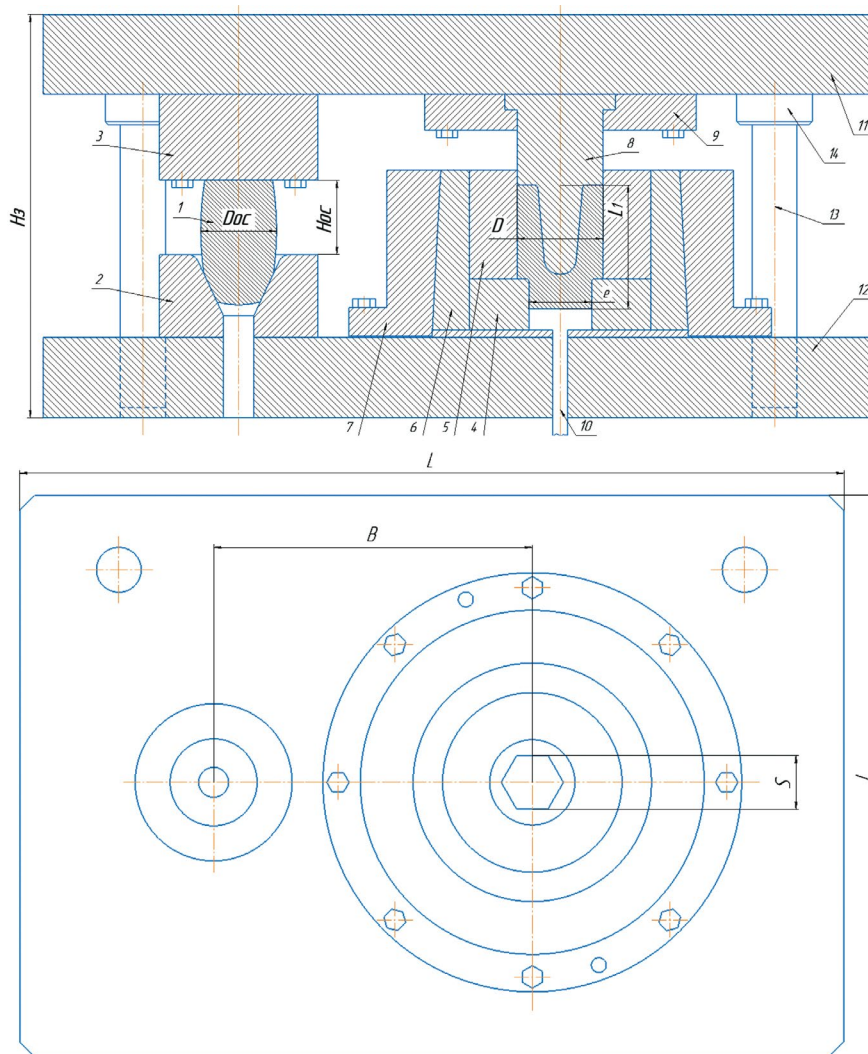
Штамп для горячей штамповки колпачковой гайки:
